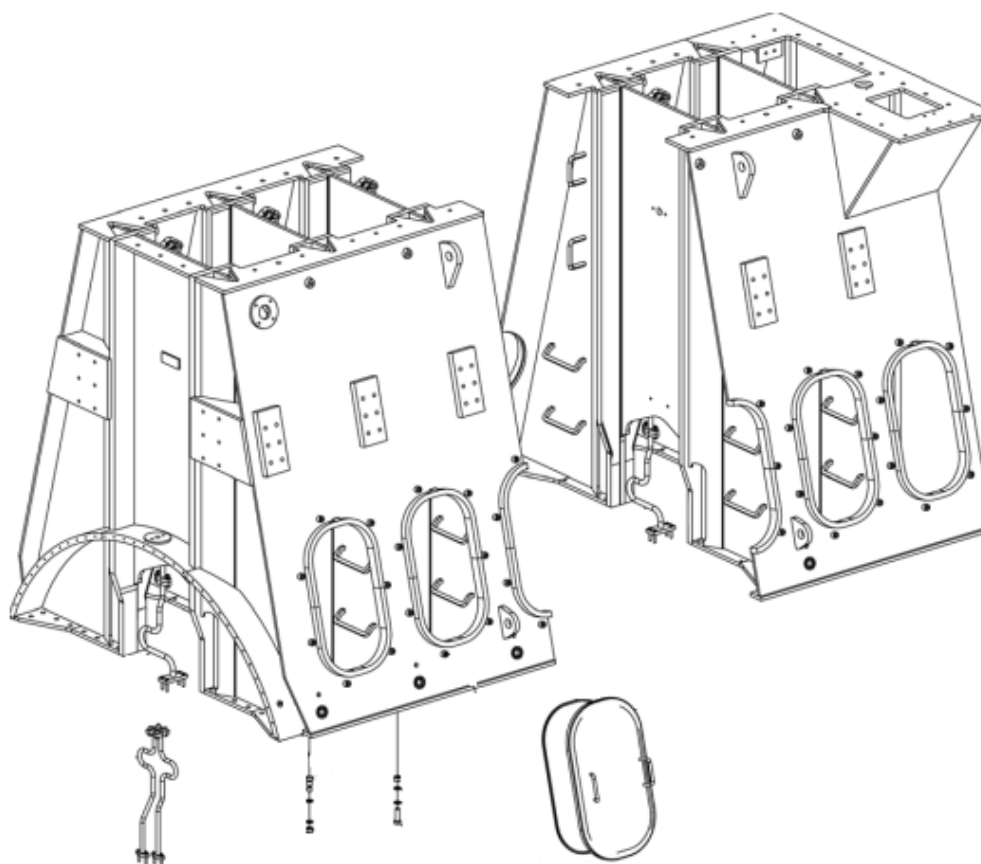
Фундаментна рама двигуна MAN 6G40ME-C9.5
